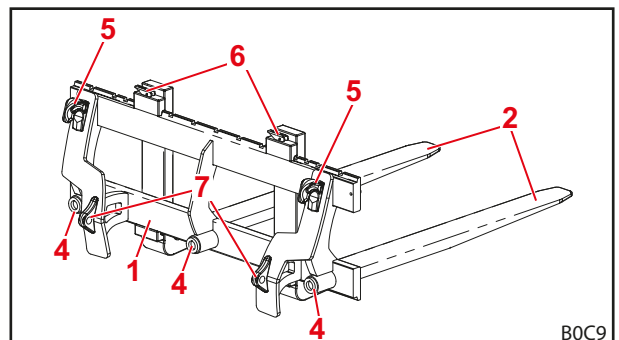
Конструкция вилок для поддонов HD с втулками для зубьев – вид сзади
